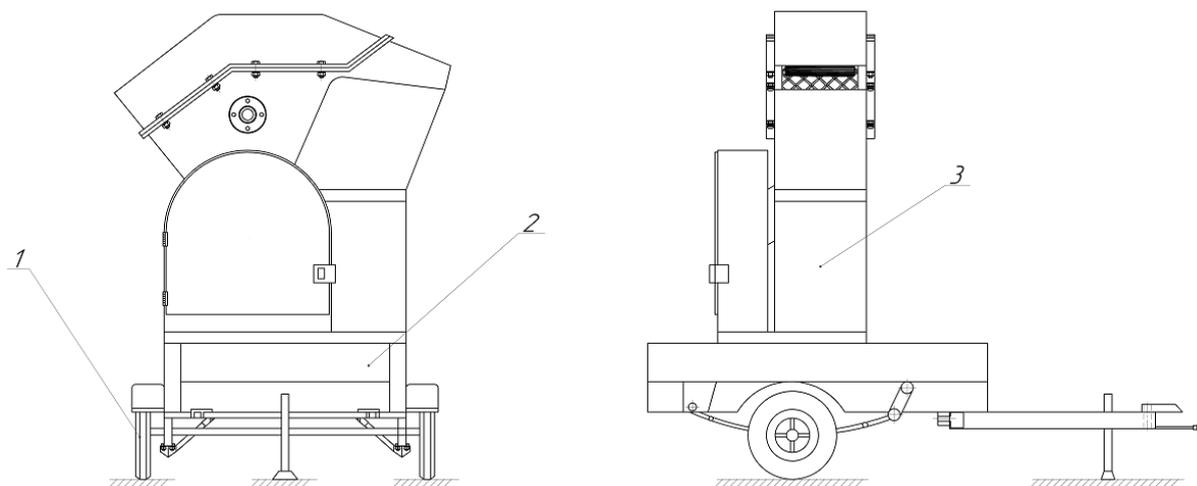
Общий вид мобильной установки для измельчения древесной зелени: 1 – колесная пара; 2 – сварная рама; 3 – отделяюще-измельчающая установка
